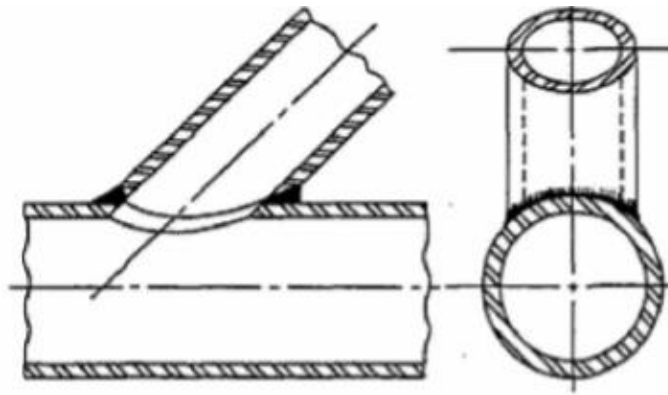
Ramificación angular soldada sin refuerzo adicional.
